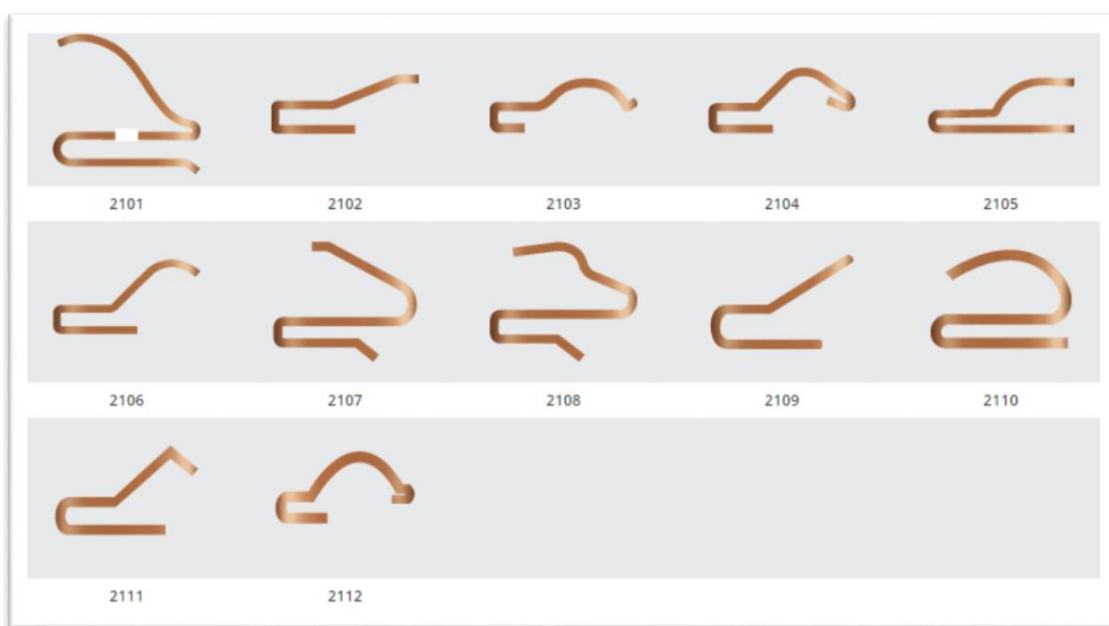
Профили металлических пружин «Clip-on mounting fingerstrips 2100»
